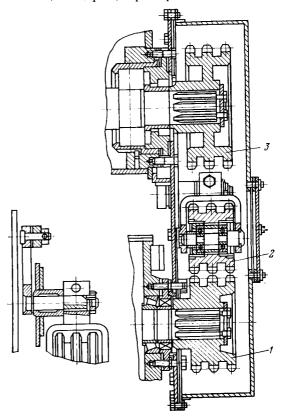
Цепная передача агрегата Азин-маш-32М:
